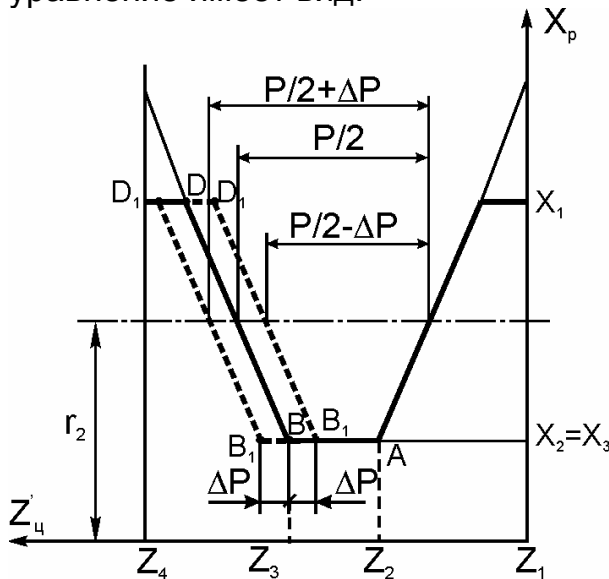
Упорный профиль резьбы с учетом погрешности шага
